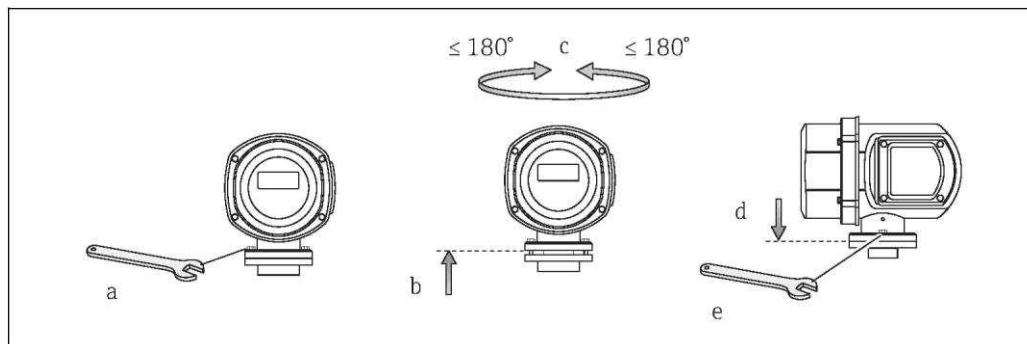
Вращение корпуса трансмиттера (полевой корпус из нержавеющей стали)
